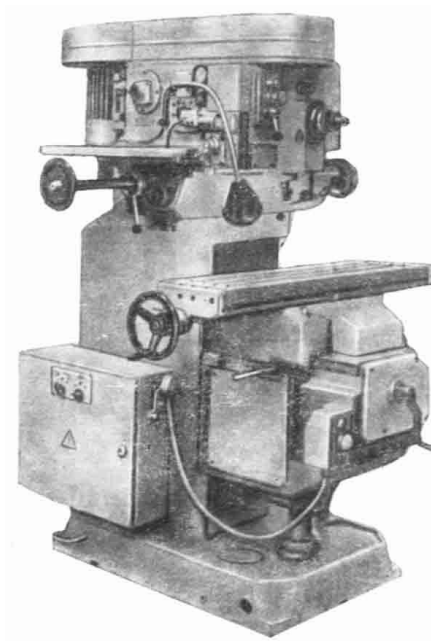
Вертикальний шпоночно-фрезерний верстат 692М
